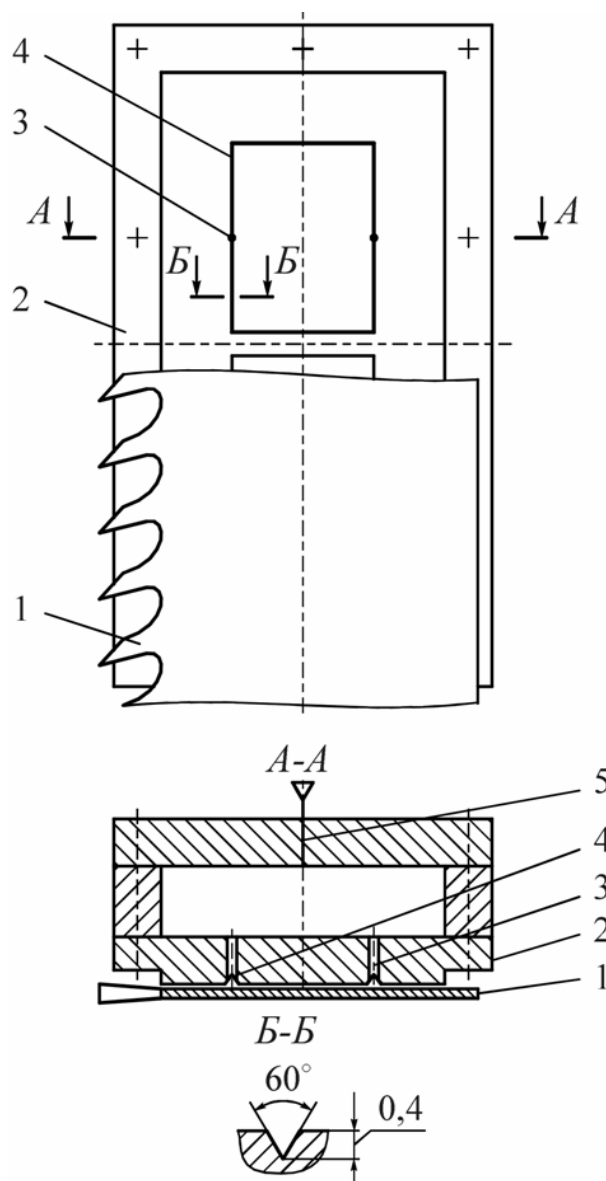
Конструкция отжимной аэроэстатической направляющей ленточнопильного станка: 1 – пила; 2 – корпус; 3 – отверстие поддува; 4 – распределительная канавка; 5 – воздухоподводящая магистраль
